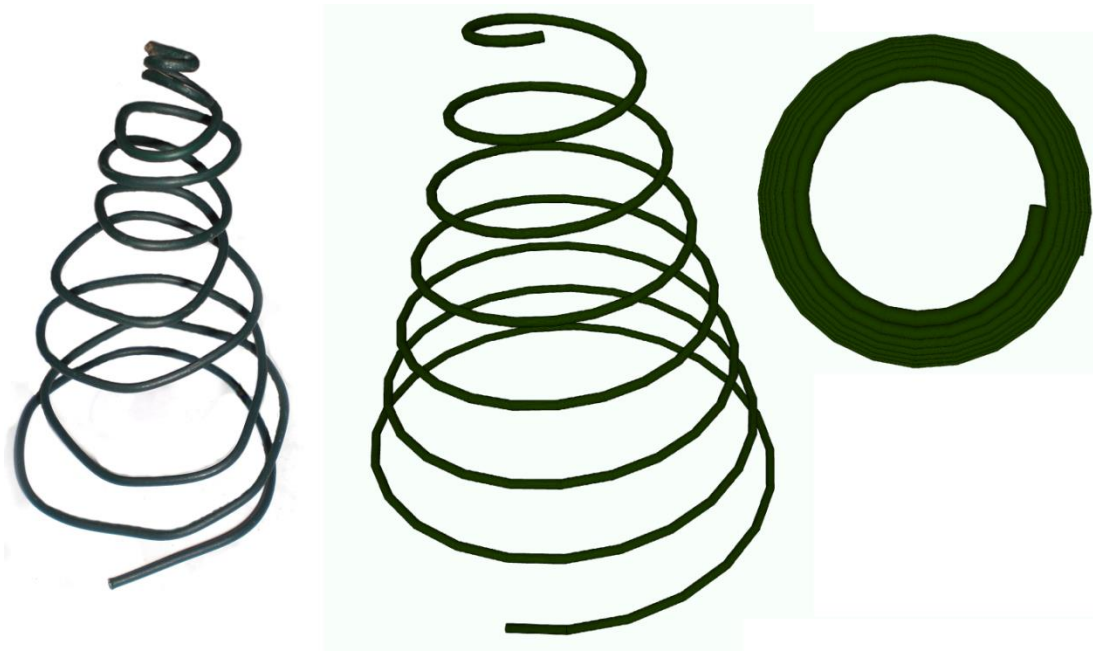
Foto Kegel (links); CAD Zeichnung Kegel (Mitte); Draufsicht CAD Zeichnung Kegel (rechts)
